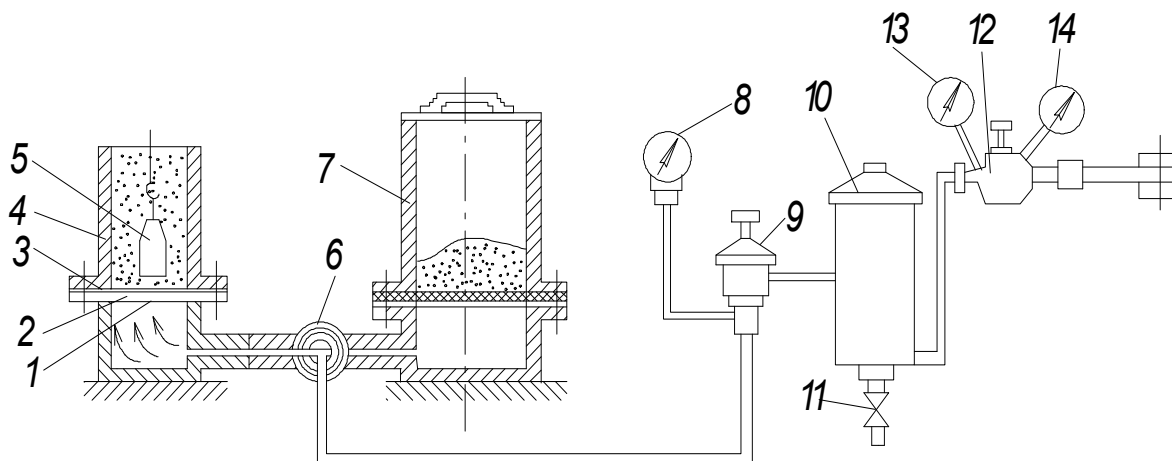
Схема установки для вихревого напыления полимеров:
